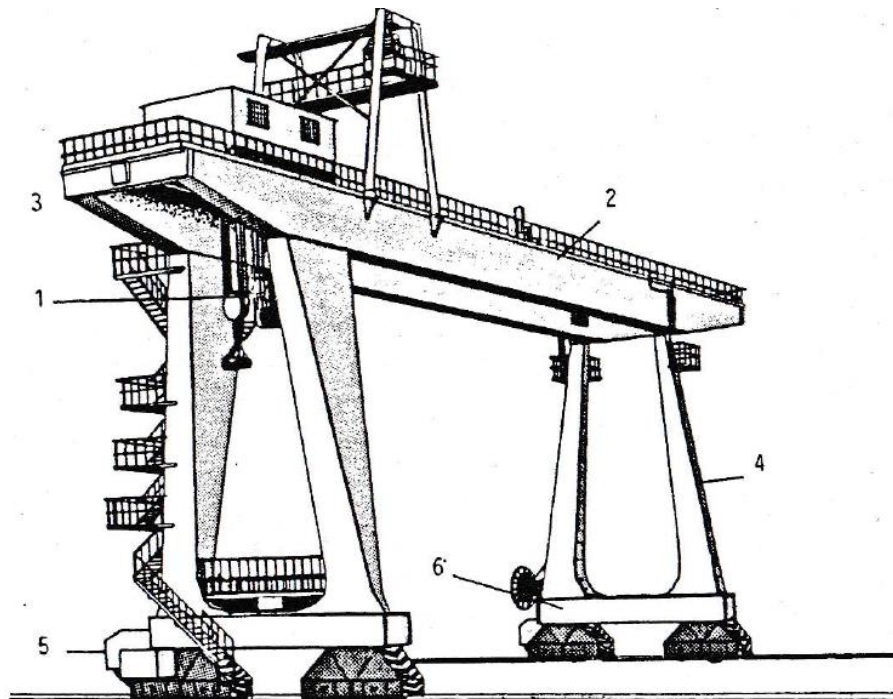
Partes principales de una grúa-pórtico: 1 mecanismo de elevación, 2 viga puente, 3 traviesa de cierre, 4 poste, 5 paquete de rodadura, 6 testero (10) (p. 262)
